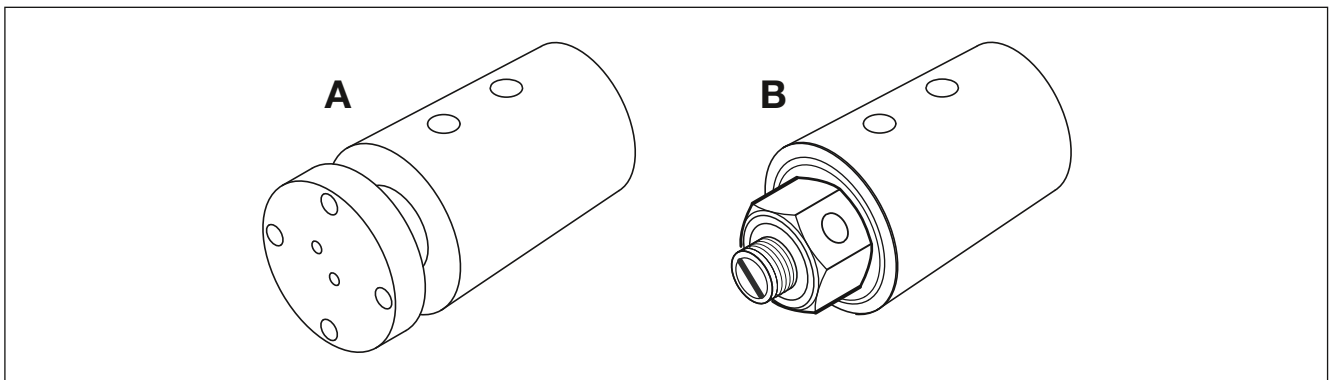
Varianten für die Befestigung an die Maschinenwelle
